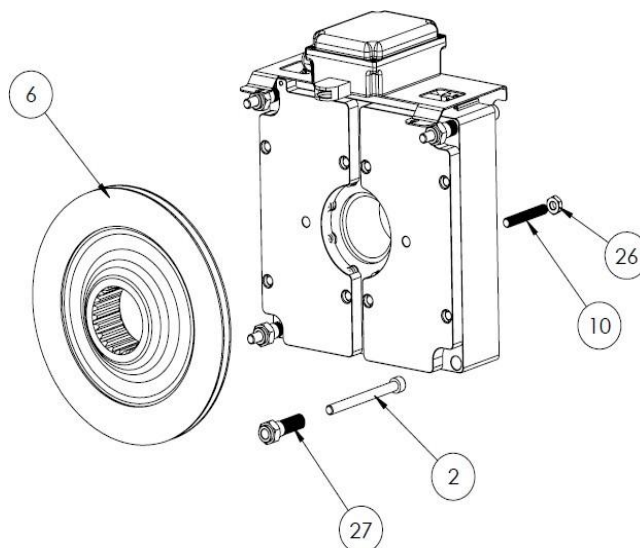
Vista en despiece del conjunto de bobinas de frenos AEMF1-2-7-8
